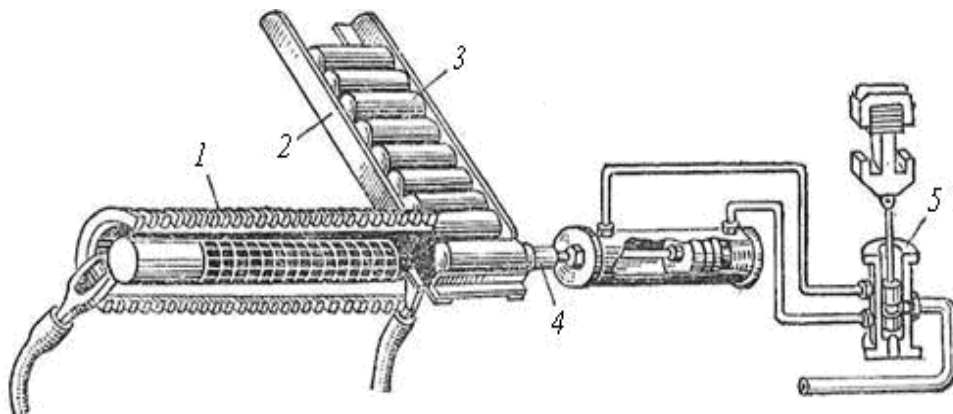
Схема індукційного нагрівання заготовок: 1-індуктор; 2-завантажувальний пристрій; 3-заготовки; 4-штовхач; 5-пневмоустановка штовхача
